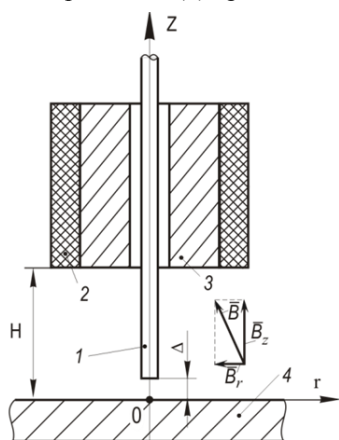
Схема для измерений компонент индукций B_z и B_r ПРМП в зоне под торцом электрода: 1 – сварочная проволока; 2 – катушка; 3 – сердечник, 4 – пластина
